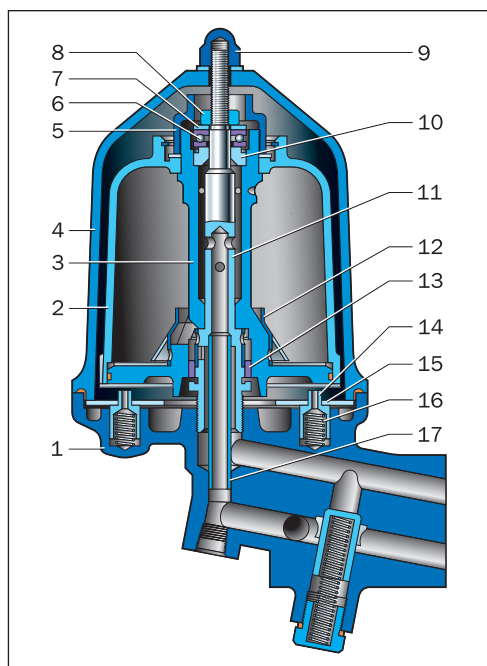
Конструкция центробежного масляного фильтра (центрифуги): 1 — корпус; 2 — колпак ротора; 3 — ротор; 4 — колпак фильтра; 5 — гайка крепления колпака ротора; 6 — упорный шарикоподшипник; 7 — упорная шайба; 8 — гайка крепления ротора; 9 — гайка крепления колпака фильтра; 10 — верхняя втулка ротора; 11 — ось ротора; 12 — экран; 13 — нижняя втулка ротора; 14 — палец стопора; 15 — пластина стопора; 16 — пружина стопора; 17 — трубка отвода масла
